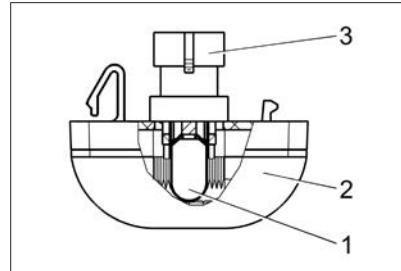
б. Фонарь освещения номерного знака (для модели 2170, 2172)
